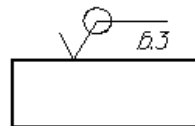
Обозначение одинаковой шероховатости поверхностей, образующих замкнутый контур
